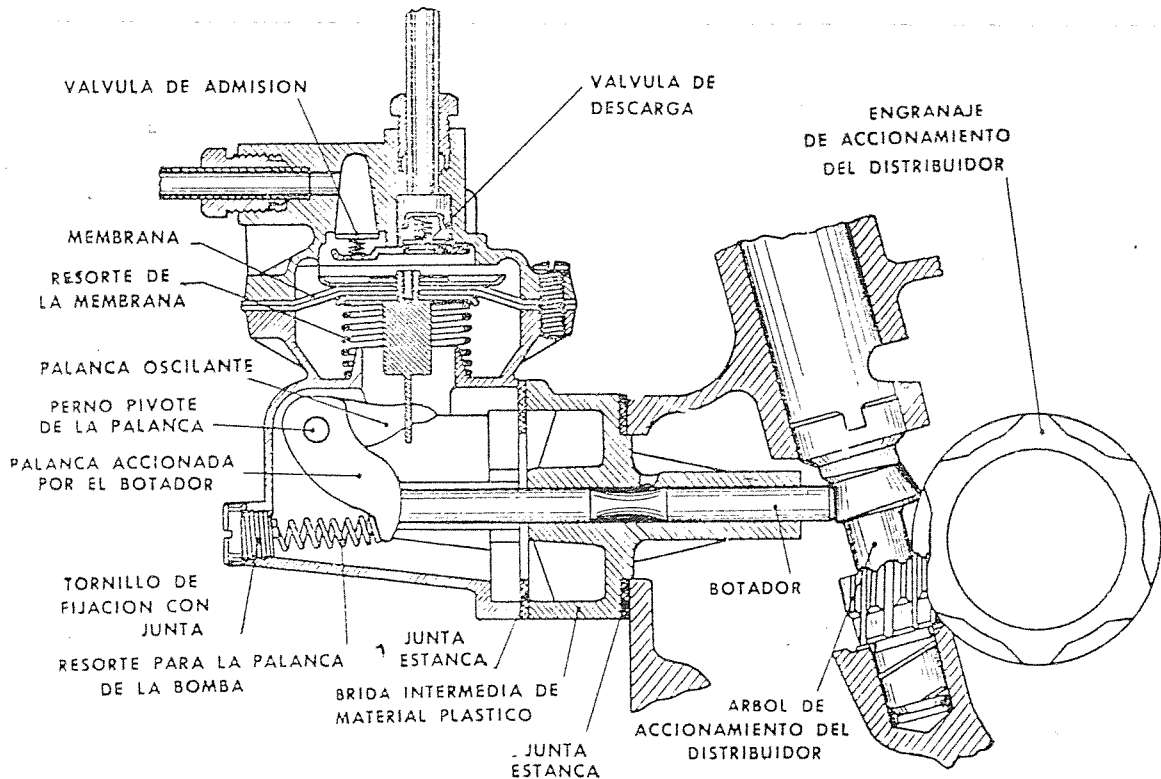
Sección transversal de la bomba de combustible instalada, con su accionamiento.
